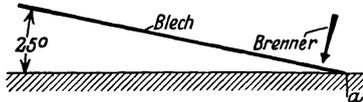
Schräge Lage der Bleche beim Schweißen.
